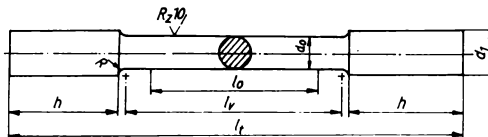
Rundprobe mit glatten Zylinderköpfen für Beißbacken
